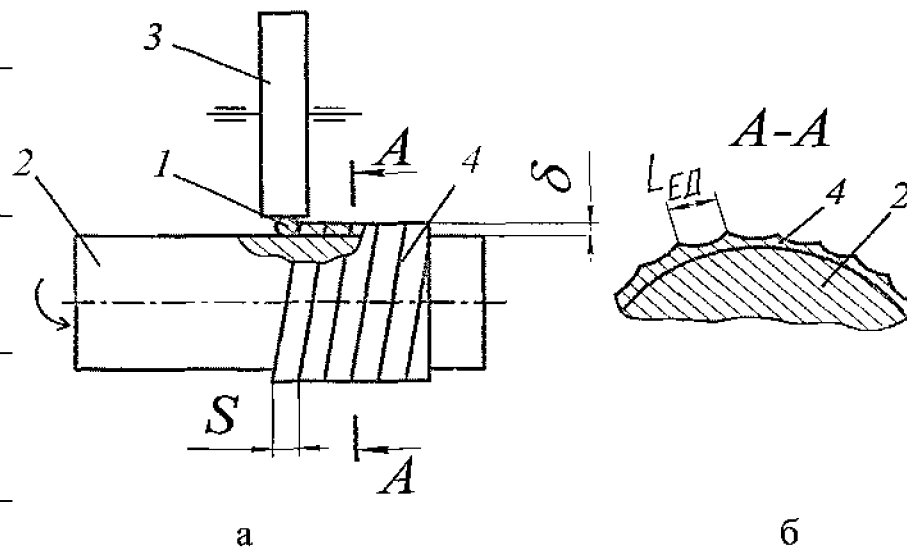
Формування одиничних ділянок металопокриття на поверхні валу:
